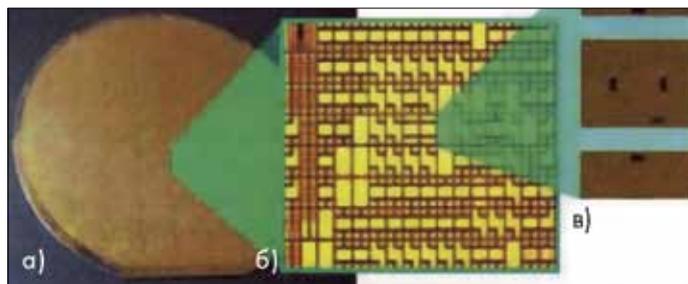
Корпусированная пластина диаметром 150 мм в сборке с крышкой (а), корпусированный кристалл (б), обратная сторона корпусированного кристалла (в)
